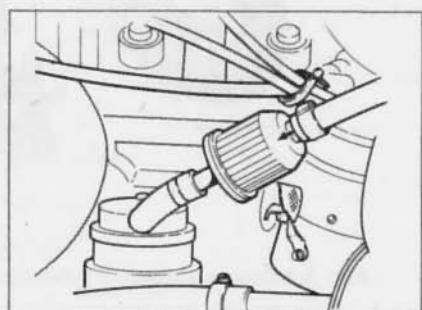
Расположение топливного фильтра и направление установки (Глава 2)
